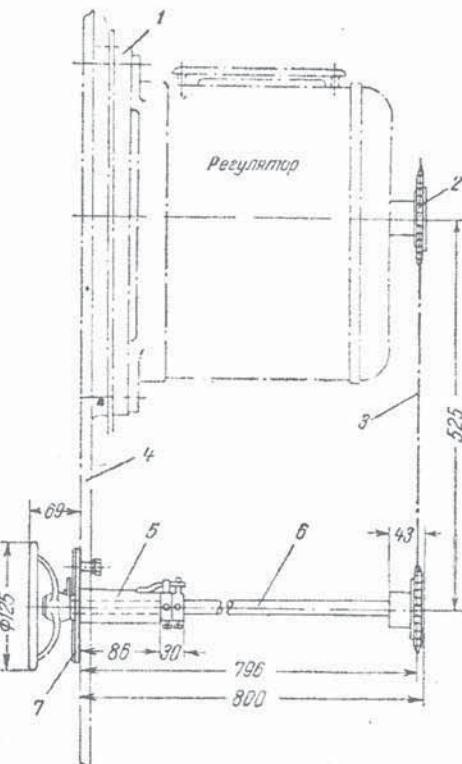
Габаритные и установочные размеры установки привода ПД-125:
